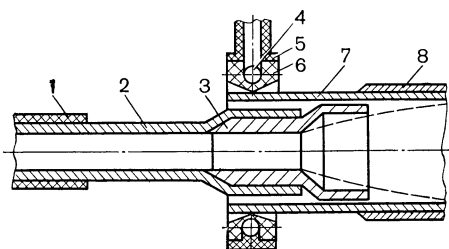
Общий вид муфты после сварки взрывом: 1 — шланг; 2 — алюминиевая оболочка; 3 — рабочая стальная втулка; 4 — алюминиевая трубка-муфта; 5 — сросток сердечника
